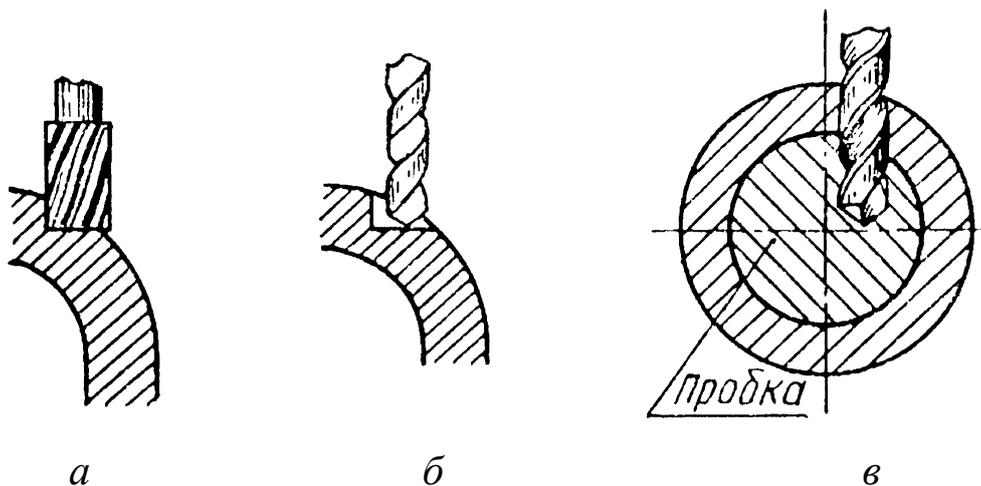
Сверление отверстий, расположенных под углом к поверхности изделия:
